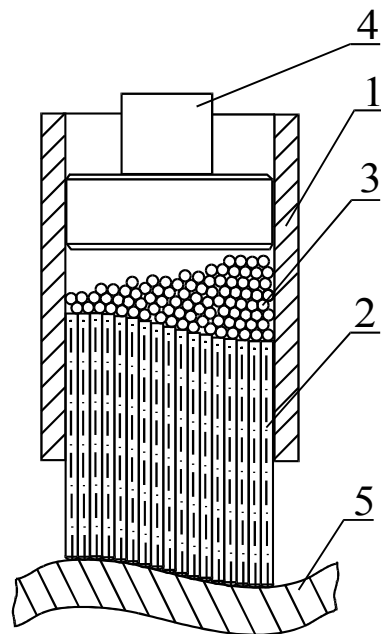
Схема многоконтактного виброударного устройства ШСУ:
